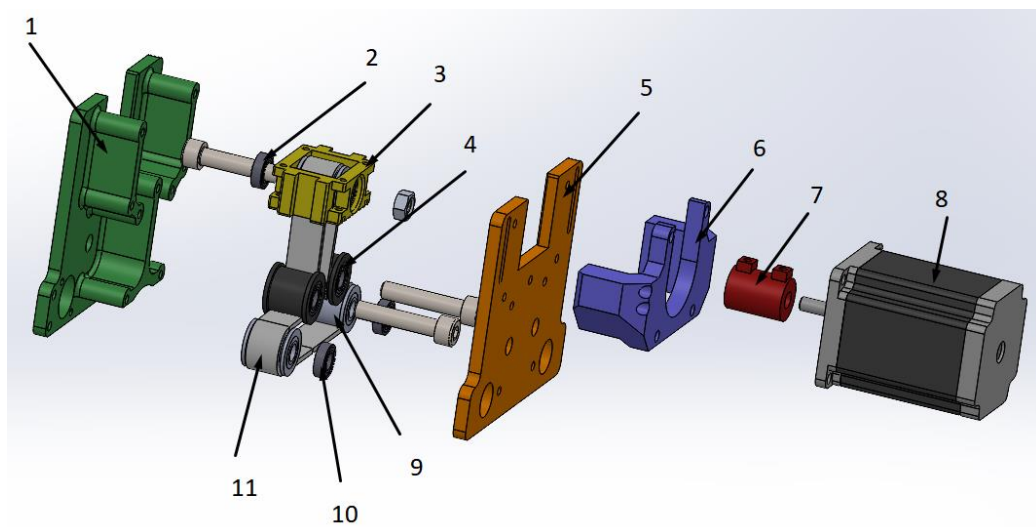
Модель приводу механізму стабілізації положення пристрою: 1) корпус приводу; 2) підшипник 608; 3) рухоме кріплення приводного шківа пасової передачі; 4) пасивні ролики; 5) кришка корпусу приводу; 6) кріплення крокового двигуна; 7) муфта жорстка; 8) кроковий двигун; 9) зубчатий шків; 10) підшипник 608; 11) пас зубчатий замкнений
